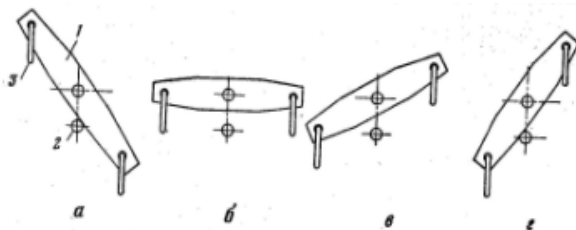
6. 9. Положення коромисла регульовочного клапана для зміни подачі палива:
